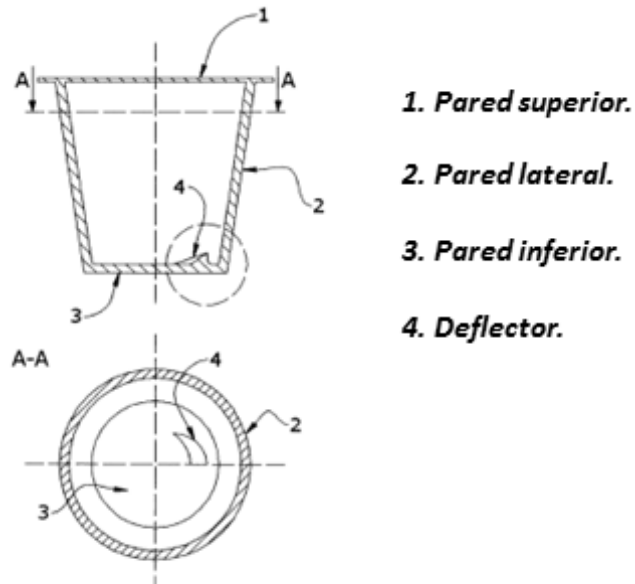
Dibujo de planta y alzado de la cápsula con el deflector de cara plana de 10° a 45°. [ES2370862]
